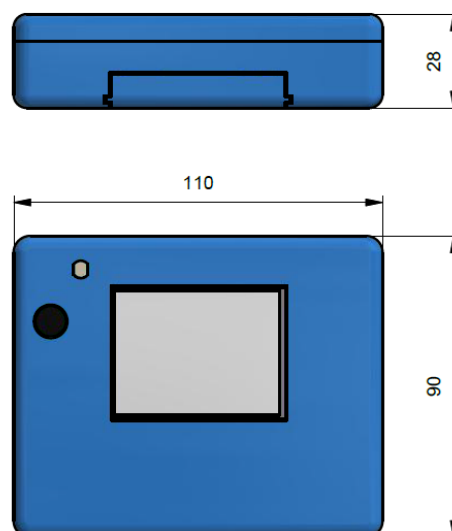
Dimensions d'encombrement du bôitier
